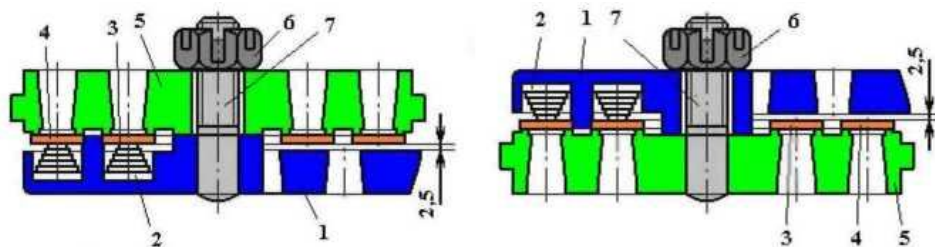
Всасывающий (а) и нагнетательный (б) клапаны компрессора КТ-6
